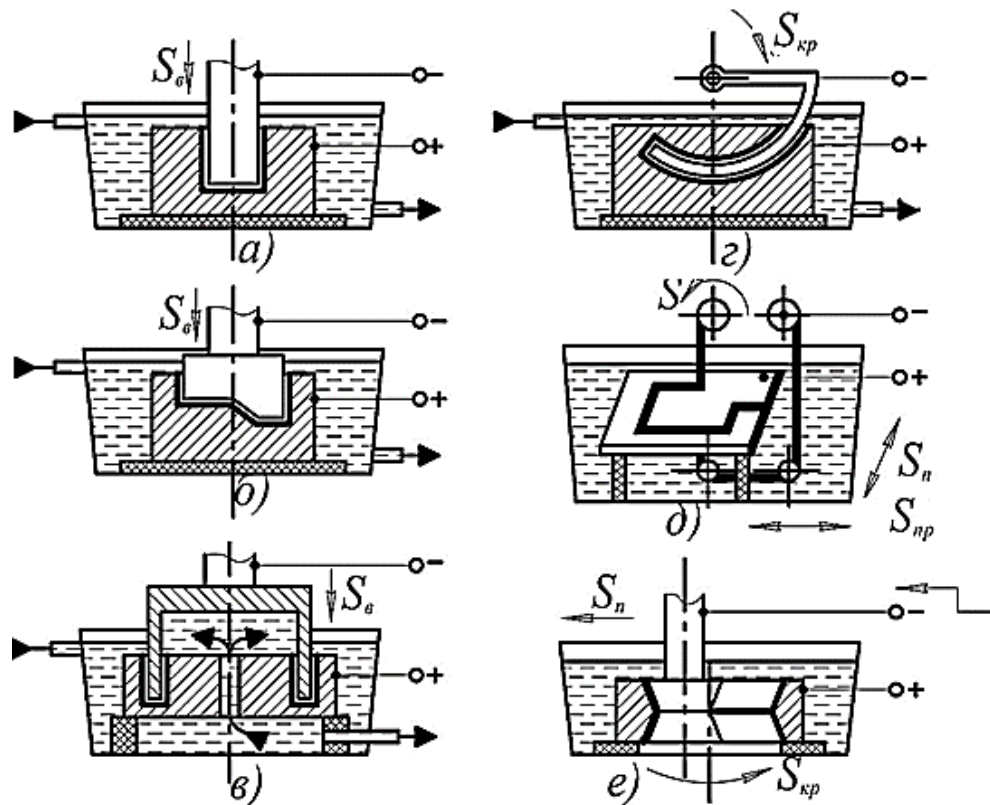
Схеми електроіскрової обробки: а – прошивання отвору; б – обробка фасонної порожнини штампа; в – прошивання отвору за способом
